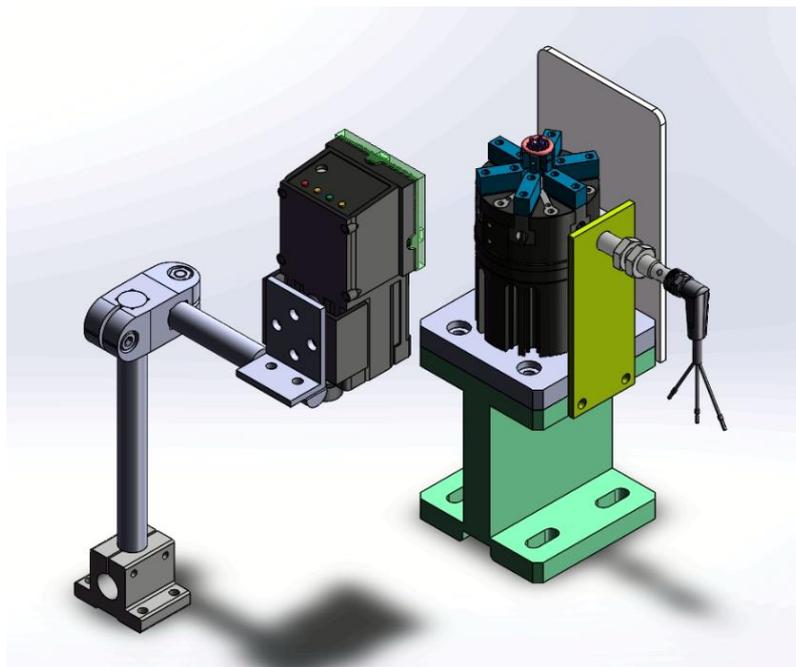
Conjunto cámara de visión. Fuente:propia
